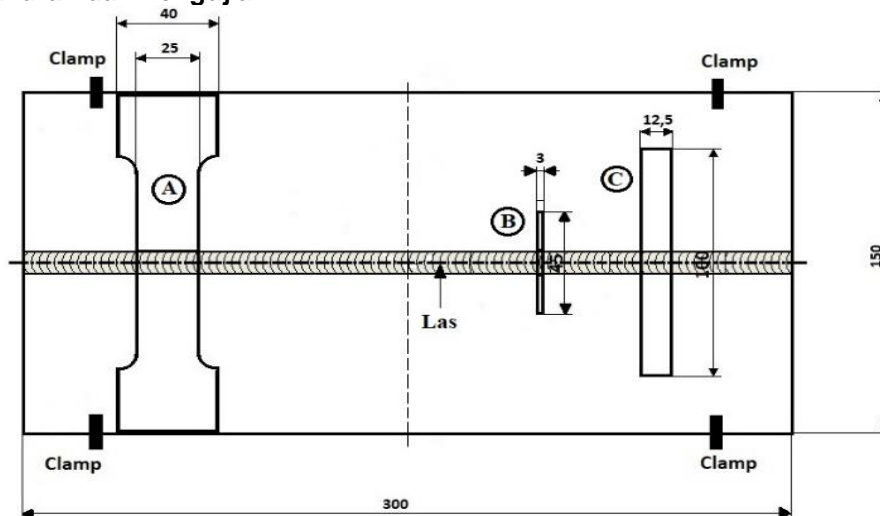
Skema pengelasan GMAW *double layer tack weld
